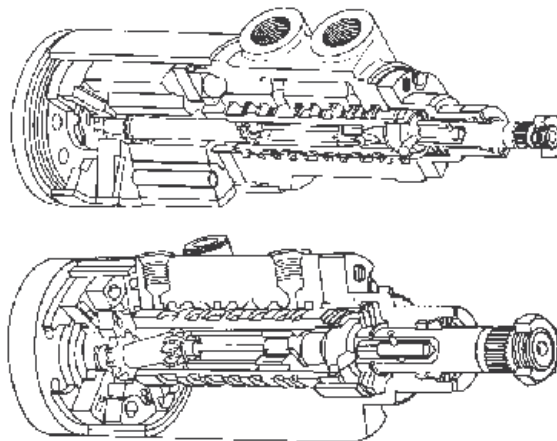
Типичный гидростатический гидроусилитель руля пластинчатого типа
